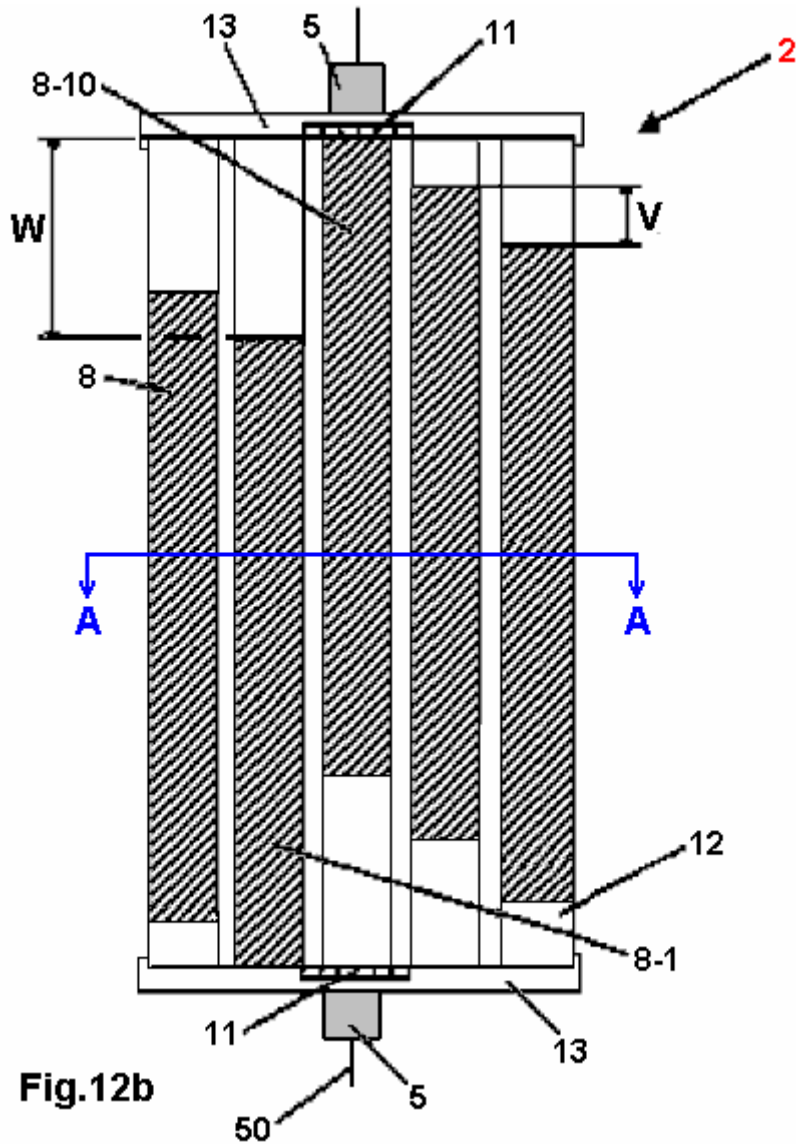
zeigt die Anordnung der Magnete des Rotors, wie in einer Ansicht senkrecht zur Längsachse des Rotors gesehen.
